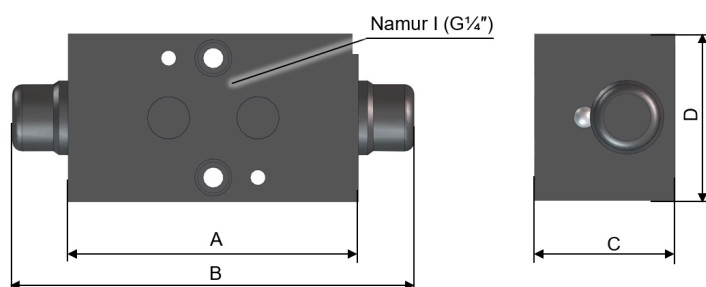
Dimensiuni principale bloc de accelerație cu efect dublu
